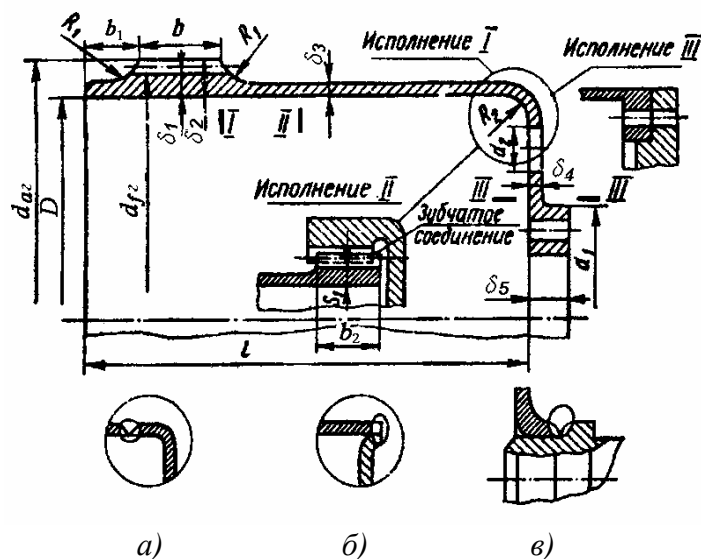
Конструкция гибкого колеса волнового редуктора
